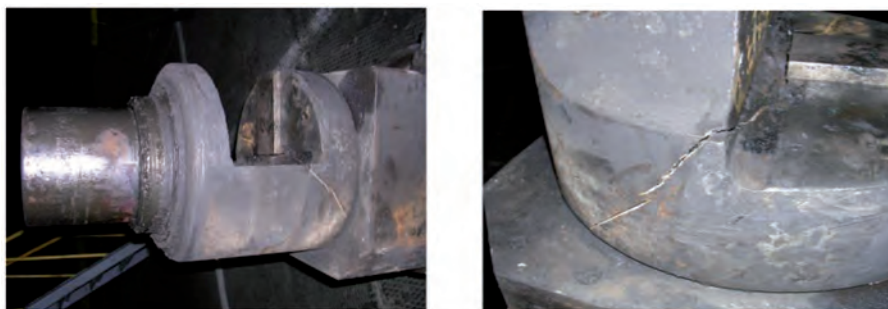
Разрушенный нижний валок рабочей клетки стана ХПТ 75
